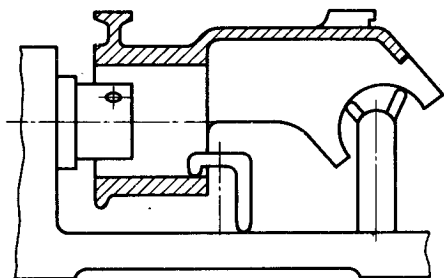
Установка рамы внутренними цилиндрическими поверхностями с пересекающимися осями
